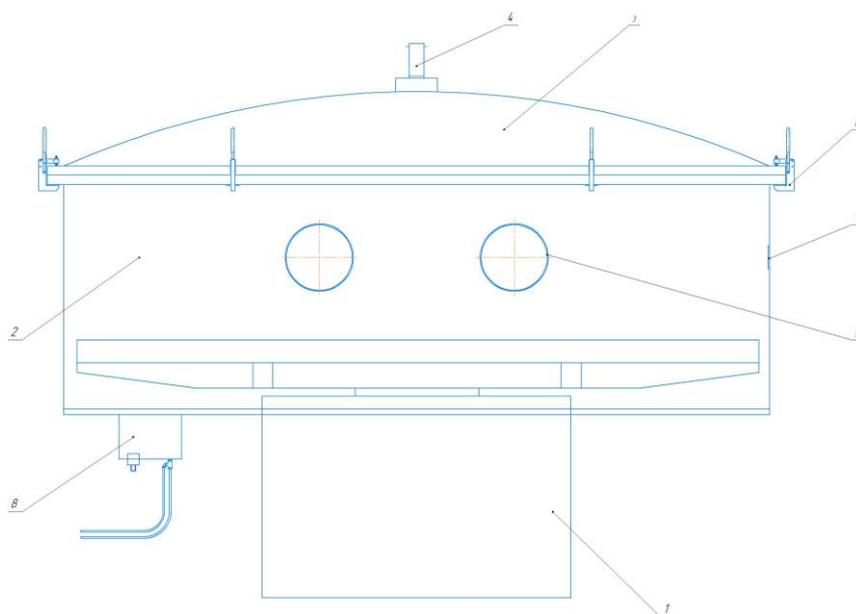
Сварочная камера, закрепленная на сварочном позиционере
